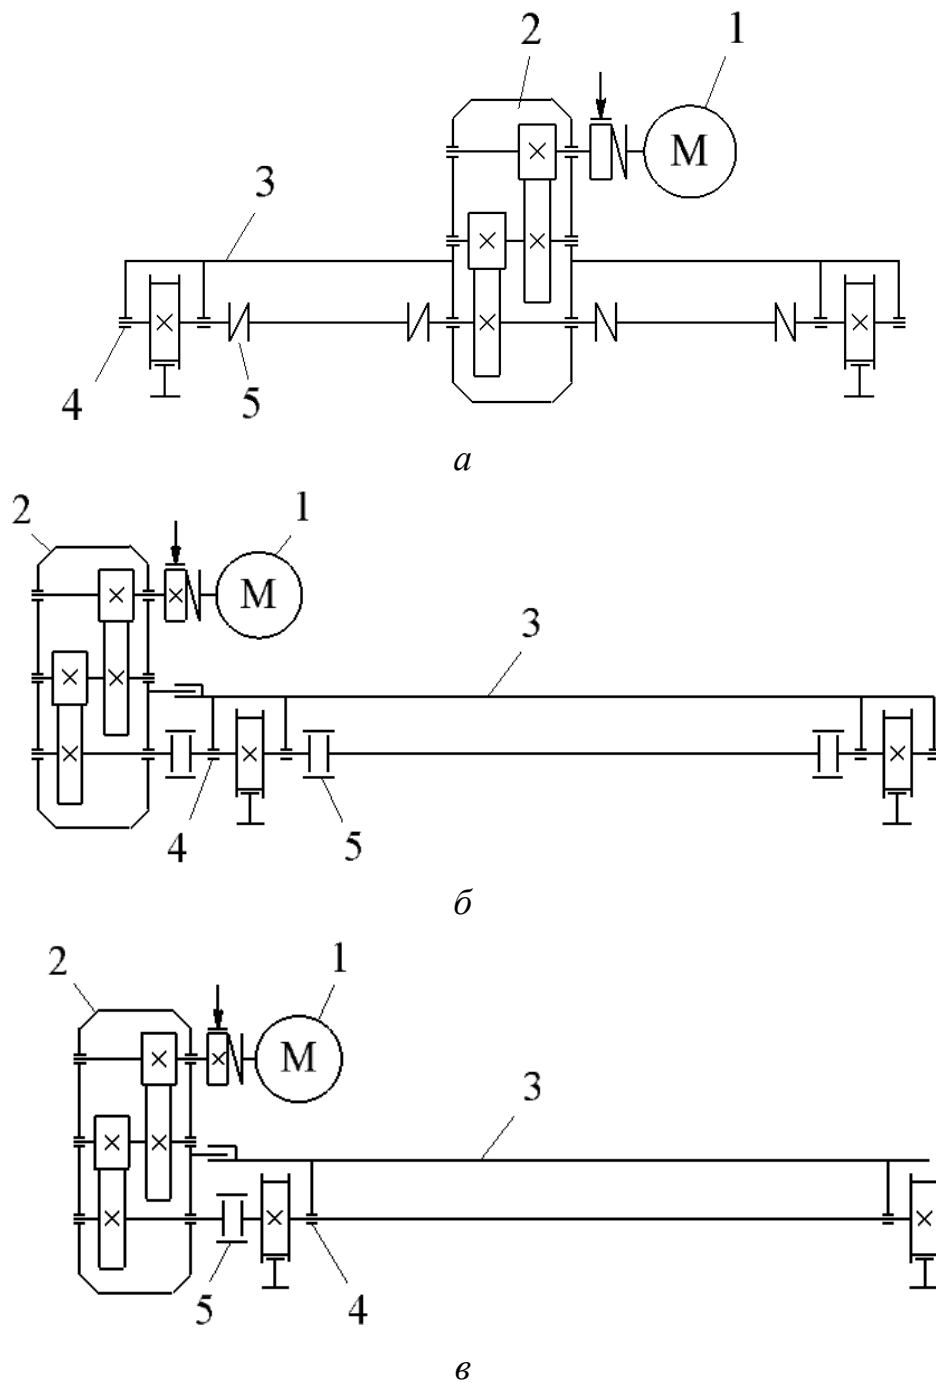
Схемы механизмов передвижения тележки: *а* — с центральным приводом; *б* — с консольным расположением привода; *в* — с общим проходным валом; *1* — электродвигатель; *2* — редуктор; *3* — рама тележки; *4* — букса; *5* — муфта
